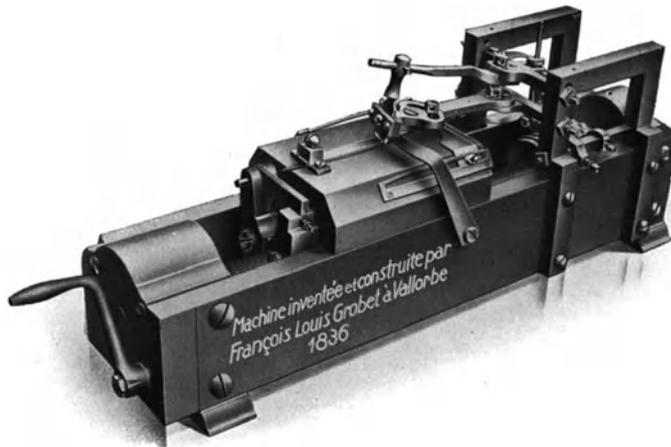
Schweizerische Haumaschine „Grobet“, 1836.
